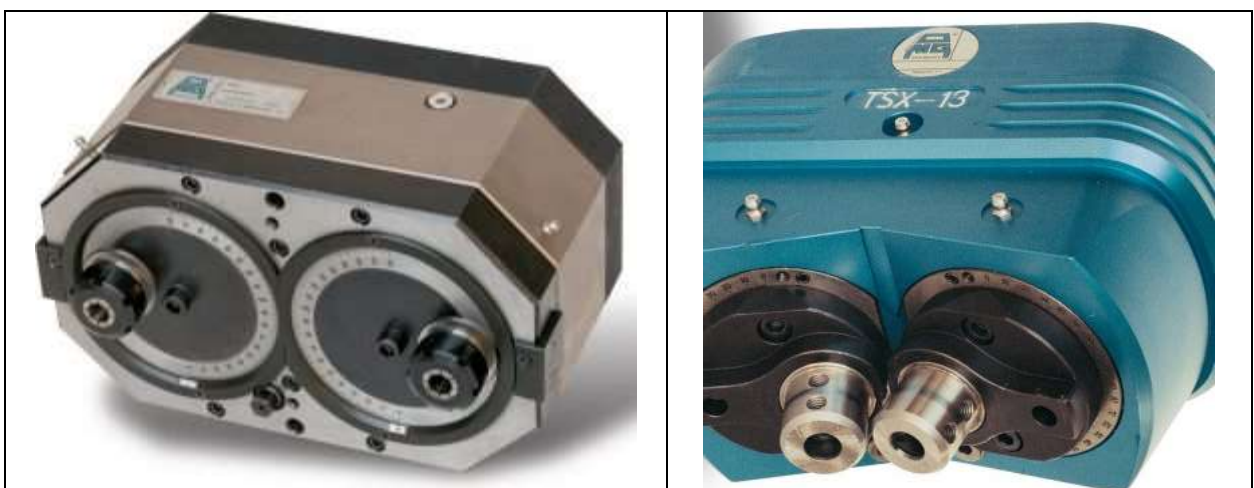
Двошпindelні фрезерні головки серії TSX (компанія OMG)
